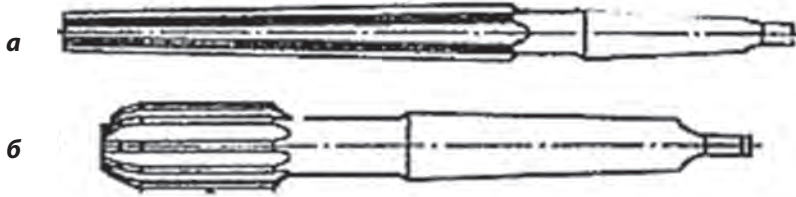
Види розгортков за формою робочої частини: а – конічна; б – циліндрична
